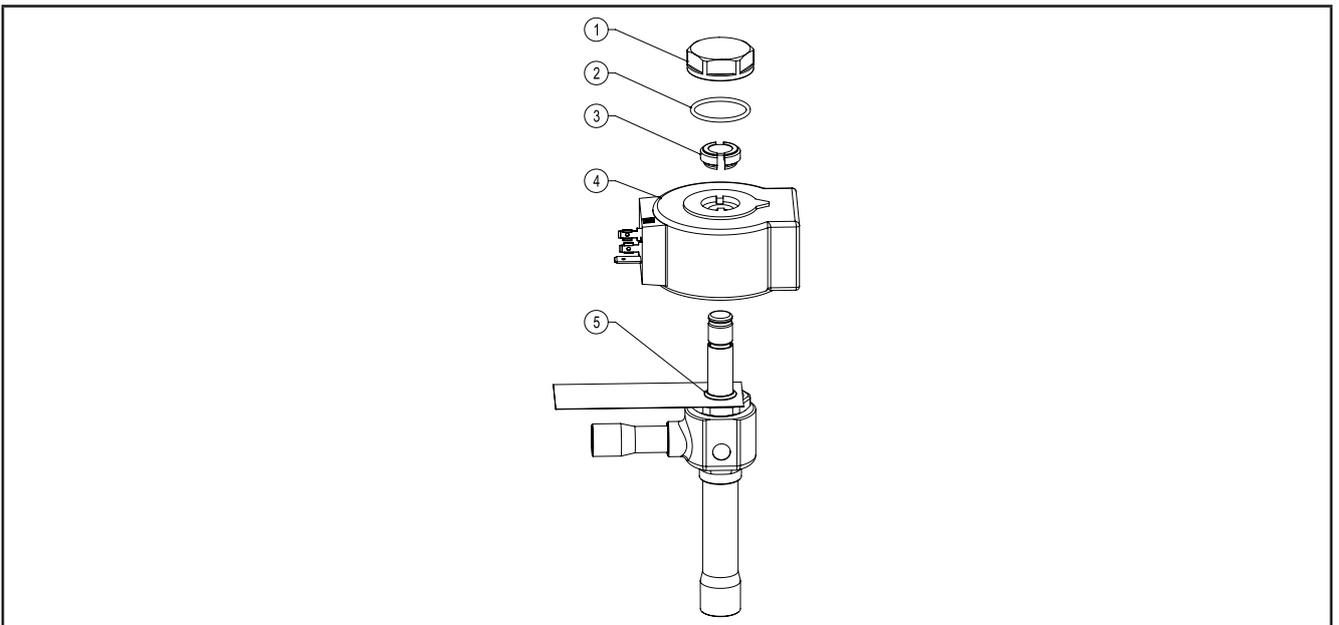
Катушка 12 Вт на корпусе 04/M12
